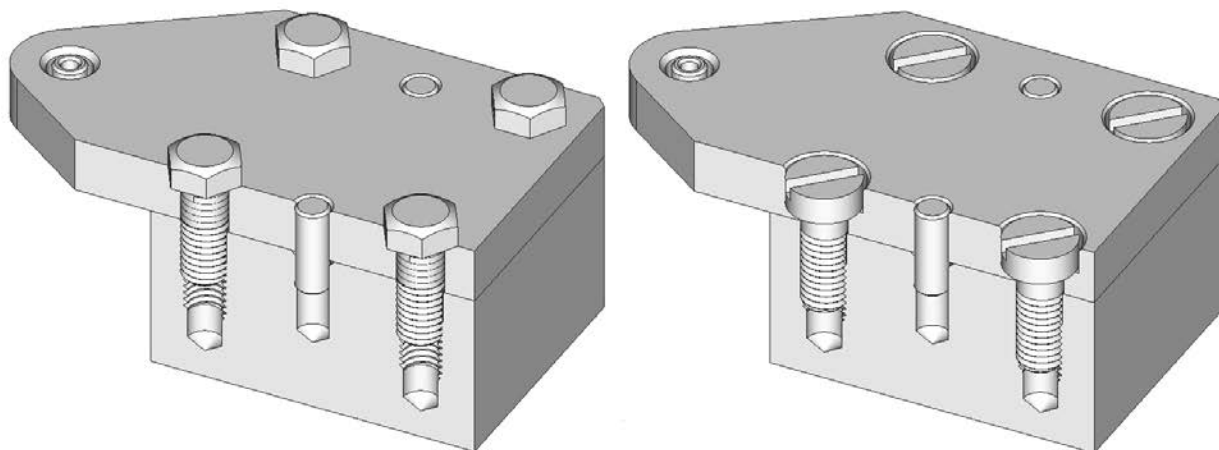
Типовое крепление кондукторной плиты на корпусе
